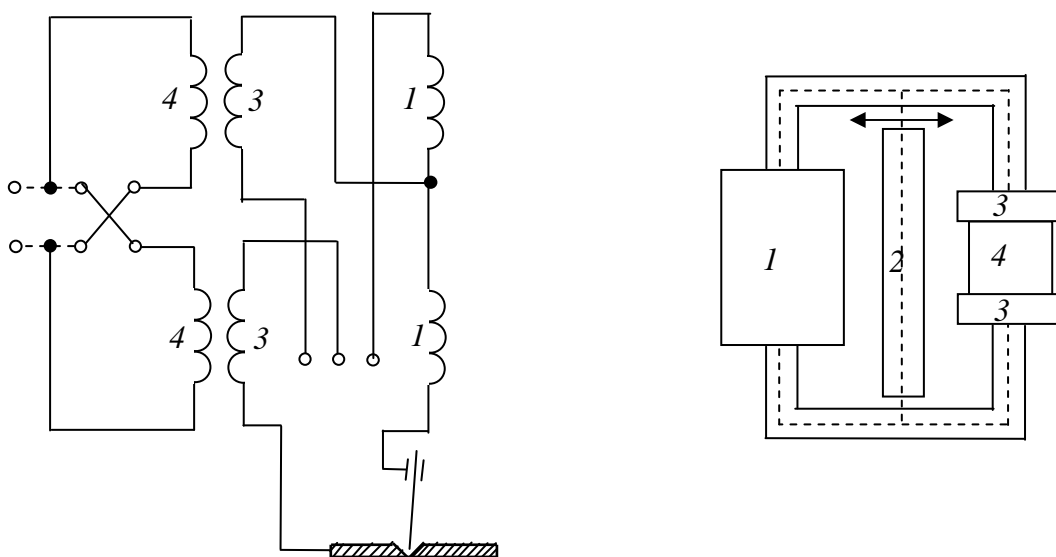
Схема сварочного аппарата с подвижным магнитным шунтом:
